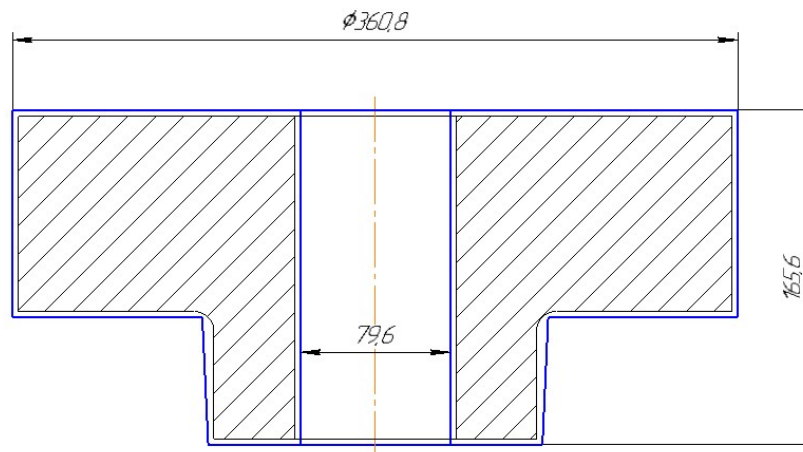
Заготовка деталі "Напівмуфта"
